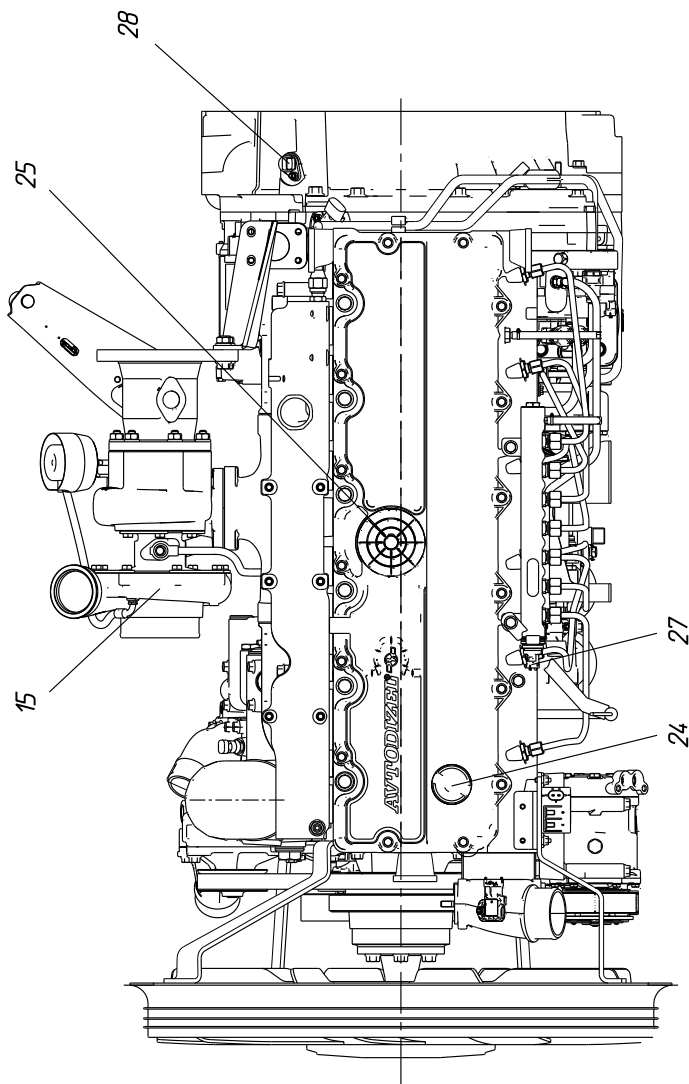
Расположение агрегатов и узлов двигателя ЯМЗ-55367 (вид сверху):
